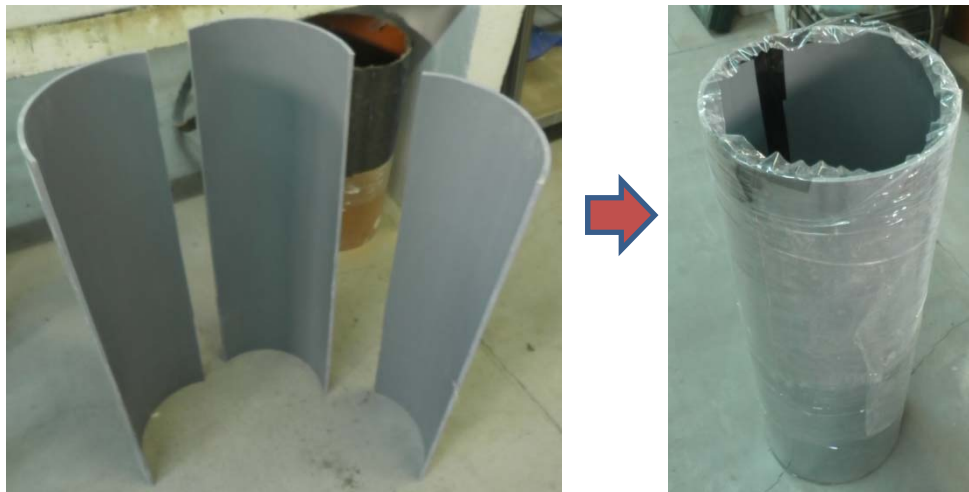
Molde utilizado para fabricar las camisas prefabricadas de CFRP.
